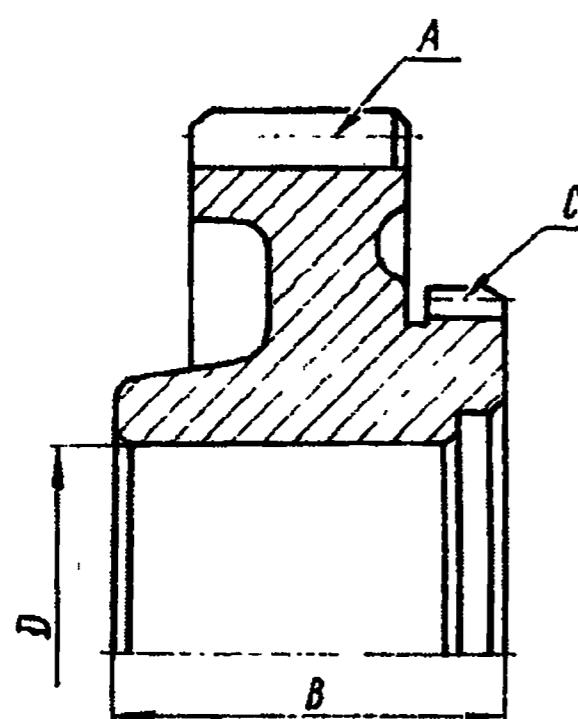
Колесо зубчатое постоянного зацепления промежуточного вала
